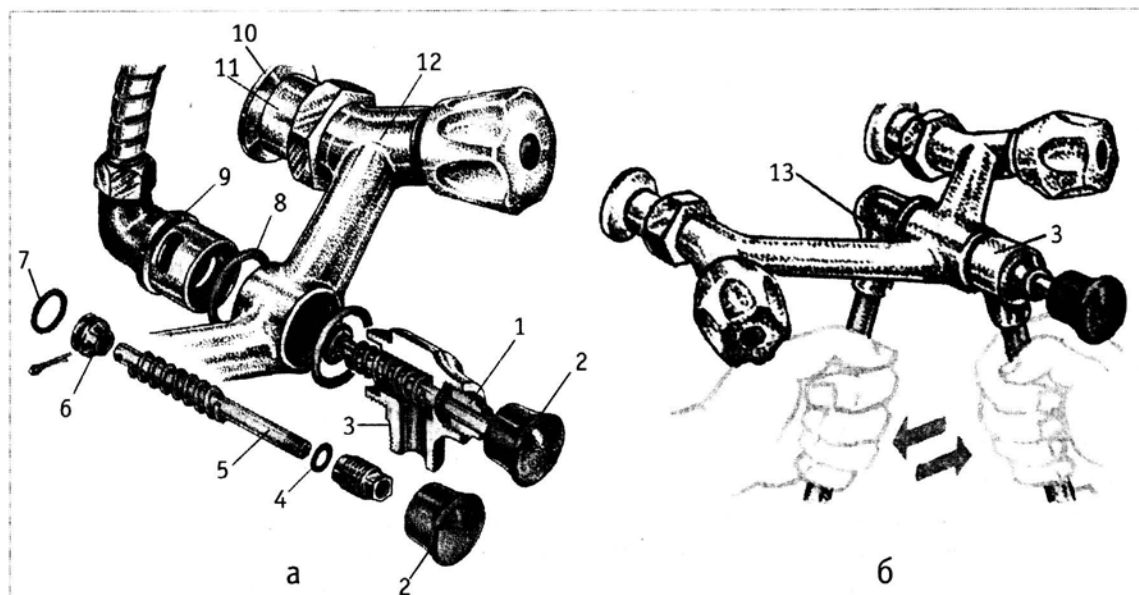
Смеситель с горизонтально расположенным кнопочным переключателем: а — детализация, б — начало разборки; 1 — спецвинт; 2 — кнопка; 3 — переходник; 4 — резиновое кольцо сальника; 5 — шток; 6 — клапан; 7 — резиновое кольцо клапана; 8 — резиновая прокладка; 9 — крышка; 10 — декоративная шайба; 11 — патрубок; 12 — корпус; 13 — угольник
